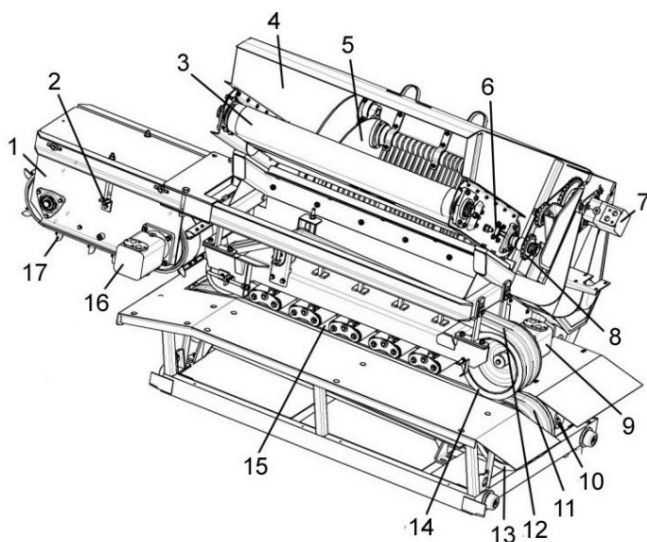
Очесывающий аппарат с промежуточным и зажимными транспортерами: 1 – промежуточный транспортер; 2, 6, 19, 23, 25 – натяжные устройства; 3 – выгрузной транспортер; 4 – кожух; 5 – очесывающий барабан; 7 – гидромотор привода очесывающего барабана; 8 – цепной привод; 9, 10 – гидромоторы привода зажимных транспортеров; 11, 12 – ремни; 13, 14 – ведущие шкивы зажимных транспортеров; 15 – верхний зажимной транспортер; 16 – гидромотор привода промежуточного транспортера; 17 – зубья промежуточного транспортера
